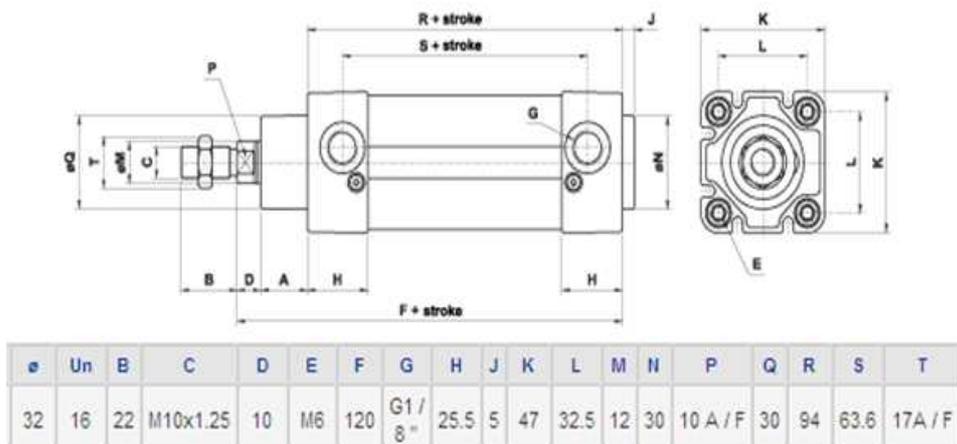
Dimensiones Pistón neumático para cuchilla suministro de producto
